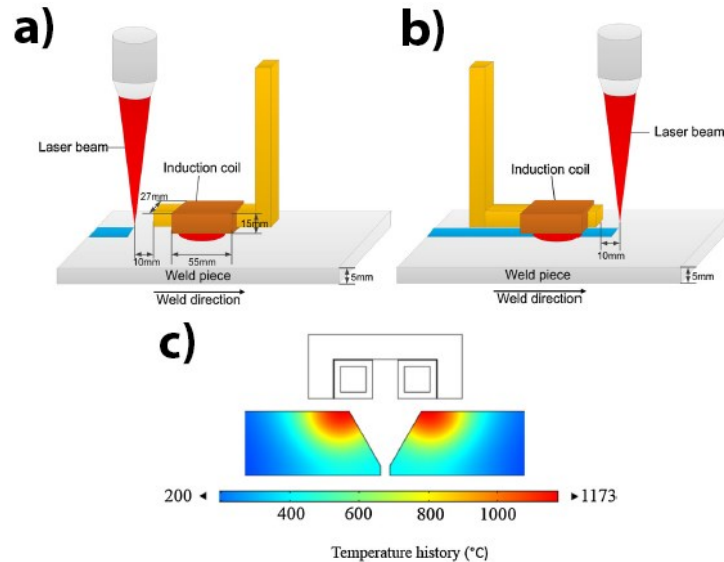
Aquecimento por indução em soldagem. Em a) Soldagem LASER assistida por pré e pós-aquecimento; b) Esquema de junta V aquecida por indução. Adaptado de Li et al. [97] e Ikram et al. [98].
